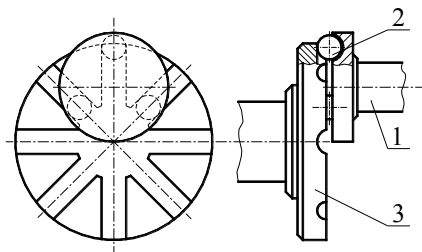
Схема торцевой передачи с ПТК: 1) входной вал; 2) шариковые тела качения; 3) выходное звено
